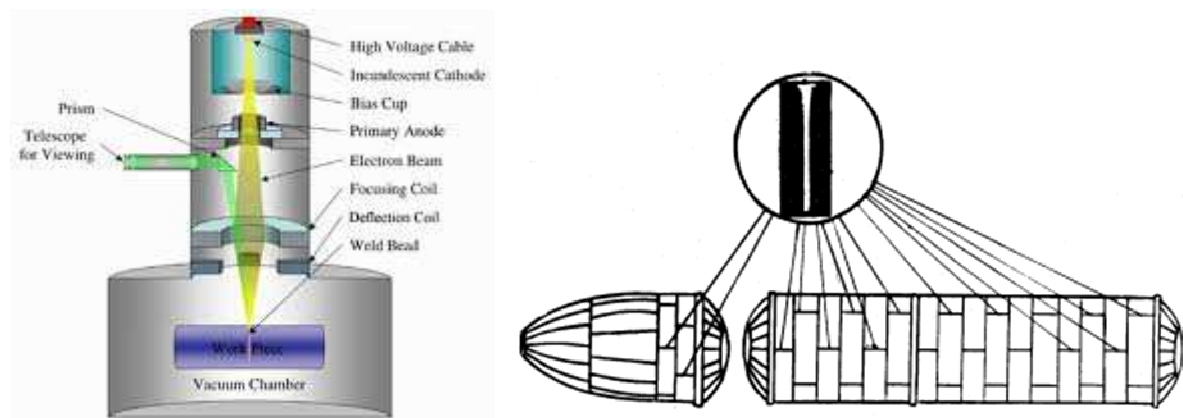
Detalhe dos arranjos das soldas logintudinais do tanque de combustível de foguetes soldada por por feixe de eletrons. Fonte: New Trends In Welding In The Aeronautic Industry
